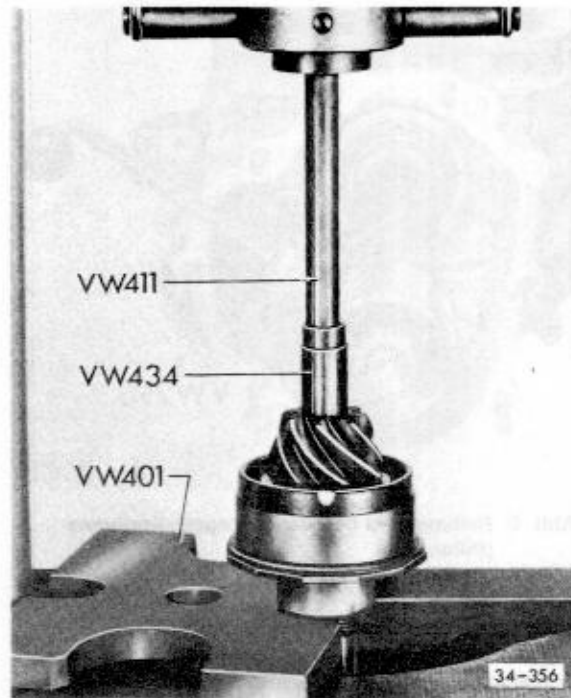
Innenringe des Doppelkegelrollenlagers und Innenlaufring des Nadellagers auf ca. 100° C erwärmen, aufsetzen und nachpressen
